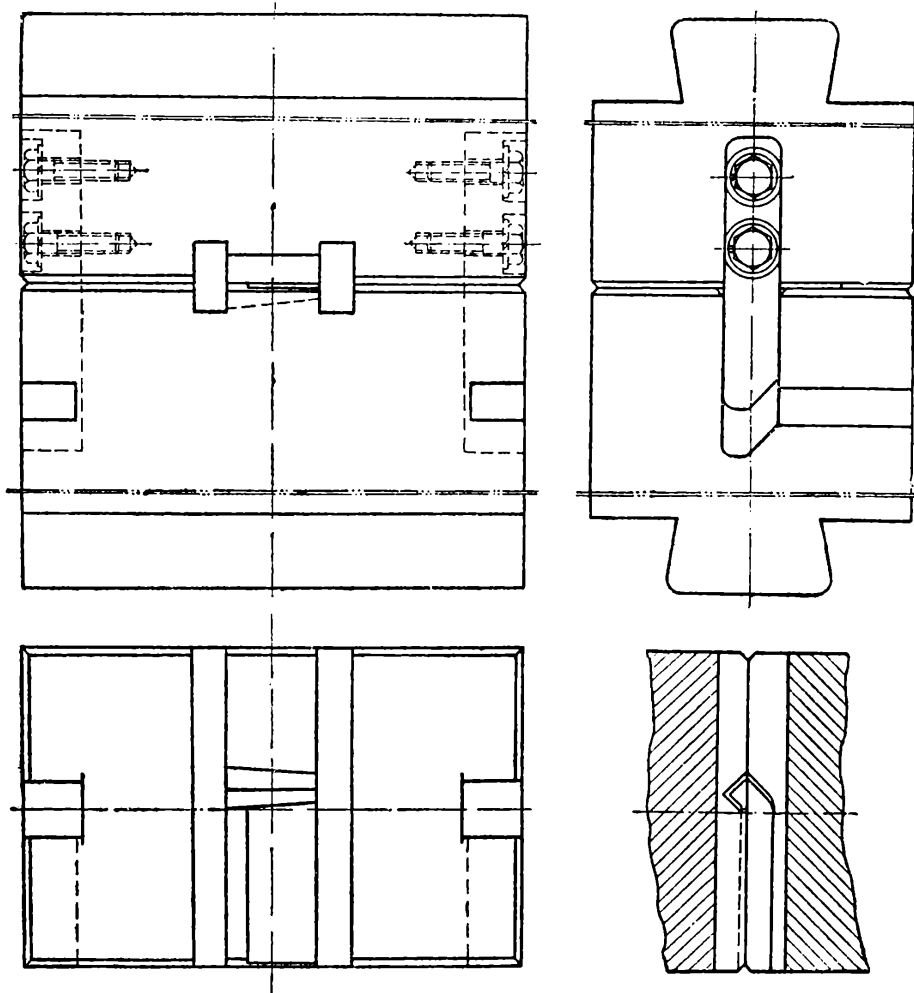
Штамп для загибки головки и формовки задних граней резца.
